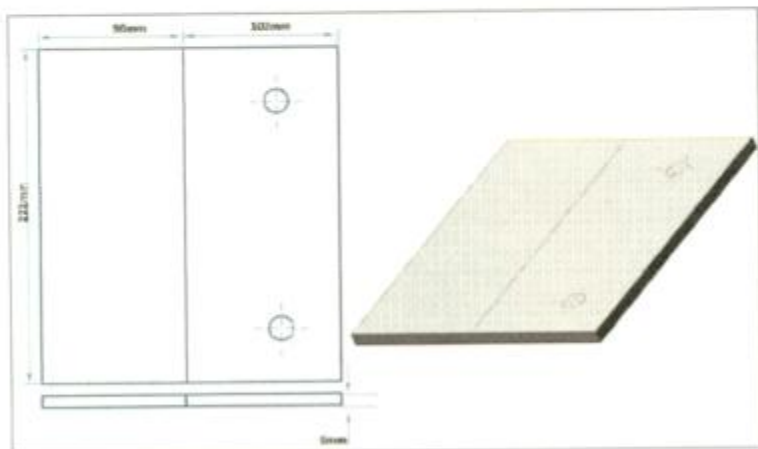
Dimensiones de la chapa soldada de aluminio.
